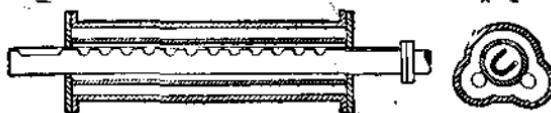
Гребенчатый опрокидывающийся жолоб.
